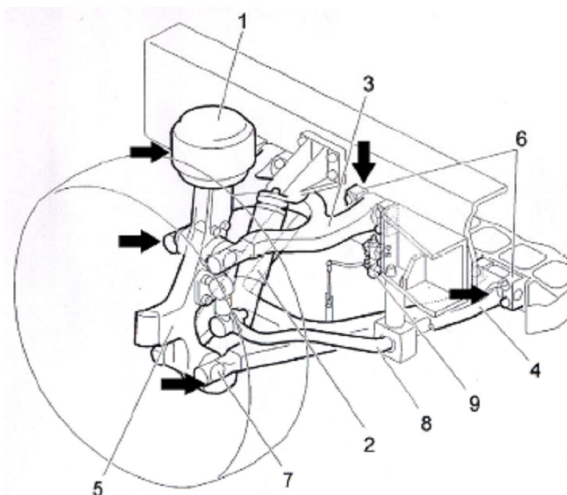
Пневмоподвеска управляемой оси автобуса и основные места её контроля: 1 – пневморессора; 2 – амортизатор; 3 – верхний рычаг; 4 – нижний рычаг; 5 – опорная стойка; 6, 7 – резинометаллические втулки; 8 – стабилизатор поперечной устойчивости; 9 – кран управления подвески.
